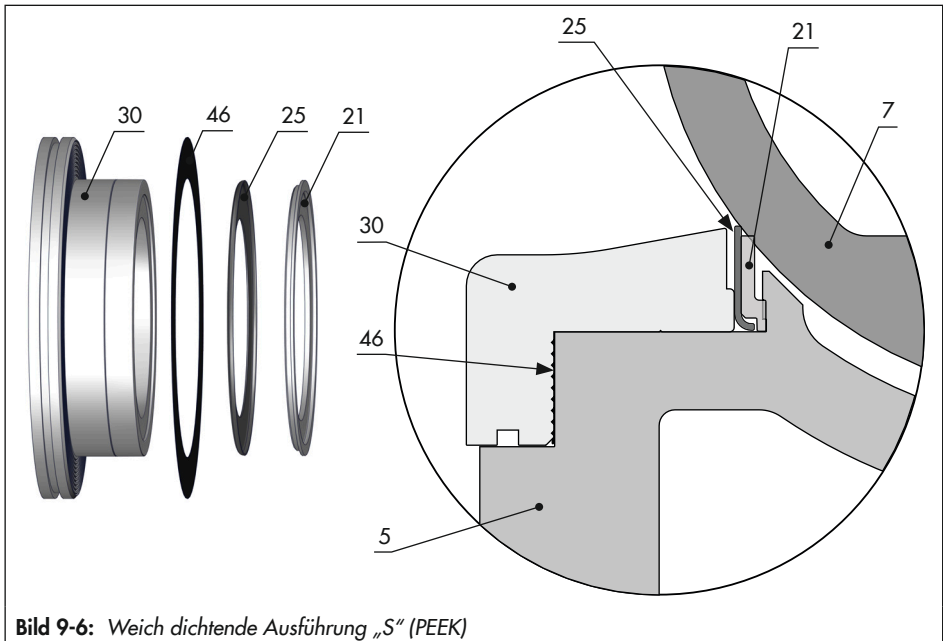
Weich dichtende Ausführung „S“ (PEEK)
